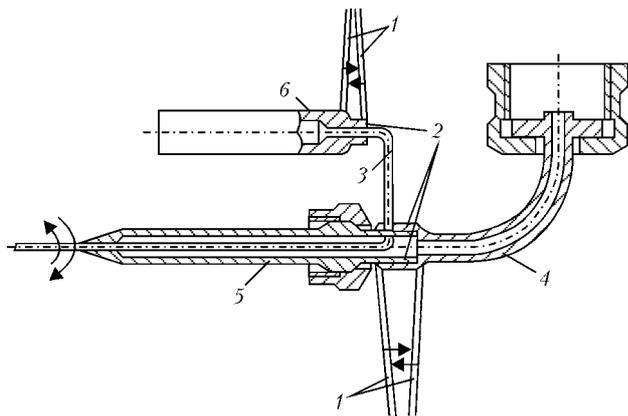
Схема пайки узла медицинского инструмента: 1 — колеблющийся электронный пучок; 2 — цилиндр; 3 — игла; 4 — патрубок; 5 — рабочий цилиндр; 6 — припой
